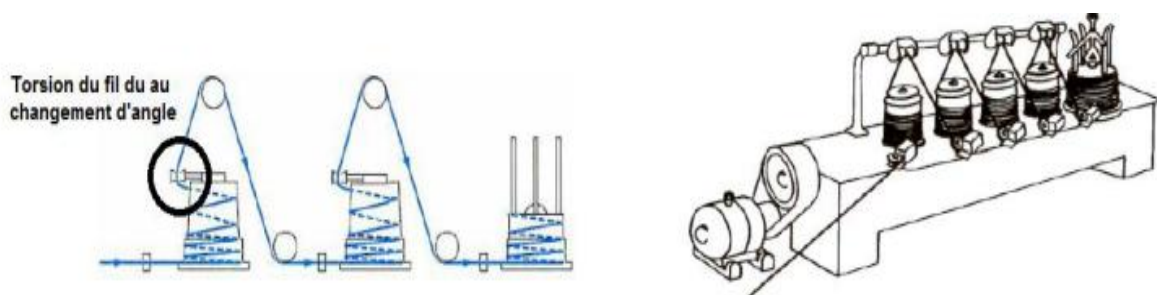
Bobinage du fil sur la machine à accumulation
